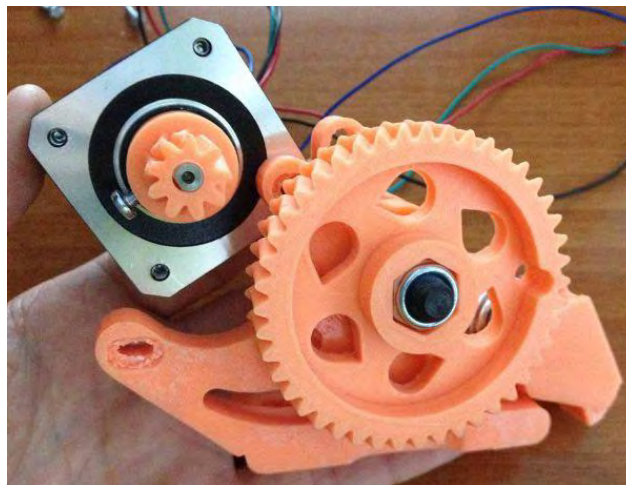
Motor fijado solo con un tornillo en la parte superior con engranaje
